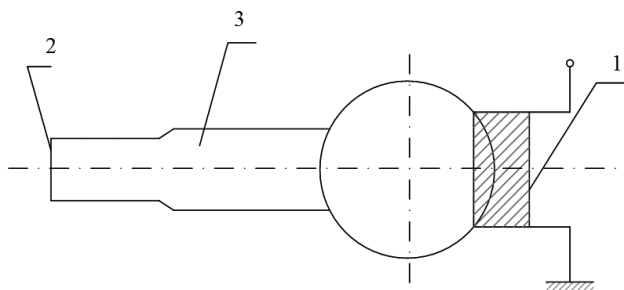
Эскиз пишущей головки: 1 – пьезоэлектрический преобразователь; 2 – сопло; 3 – чернила
